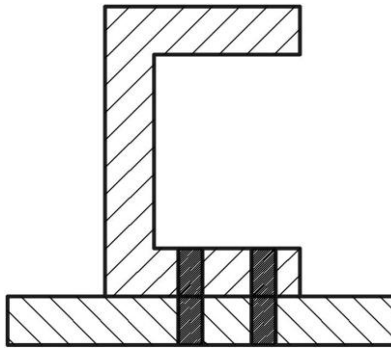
Соединение точечной сваркой полки с коробкой
